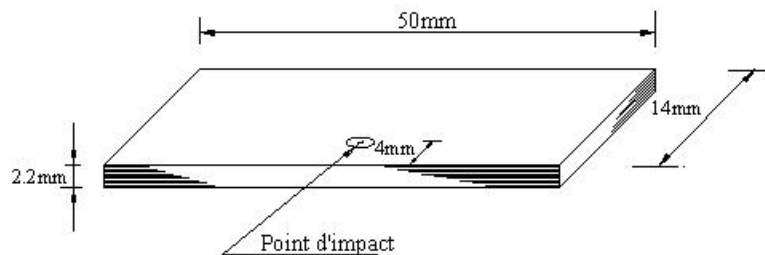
Dimensions de l'éprouvette de mittelman [4].
